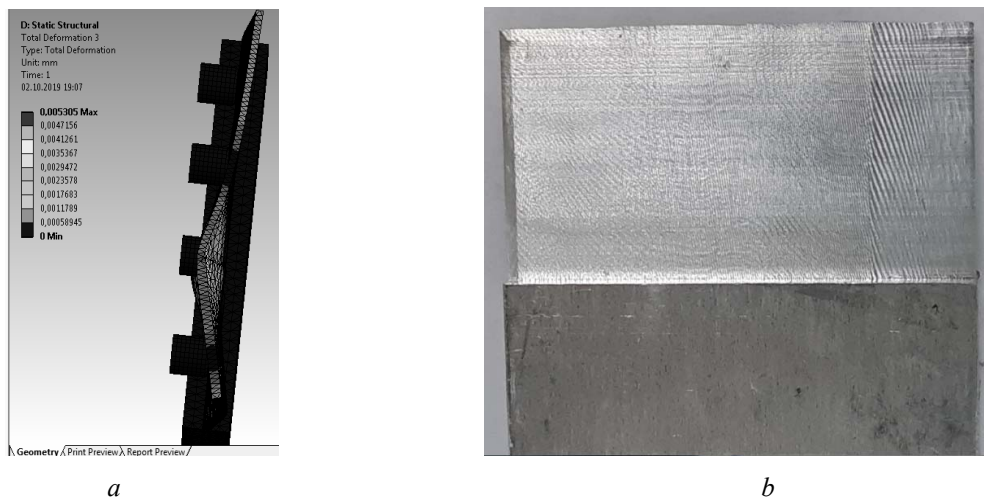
Деформации тонкостенной заготовки при фрезеровании с применением опорного модуля из 4 опор (а) и фотография обработанной поверхности (b)
